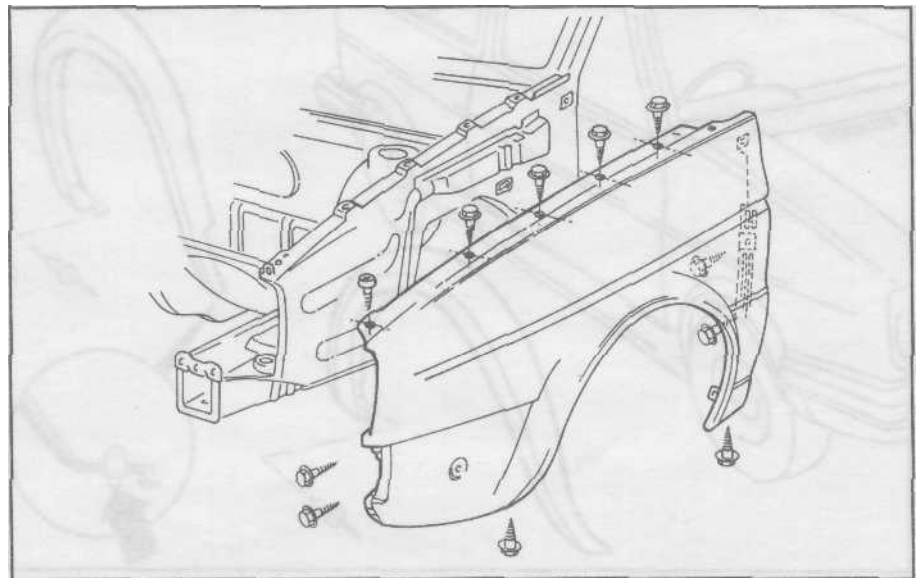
Расположение винтов крепления переднего крыла [Jetta]
